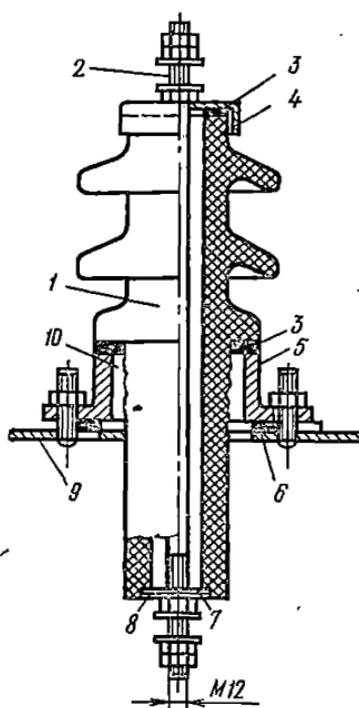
Армированный ввод 6—10 кВ наружной установки:
